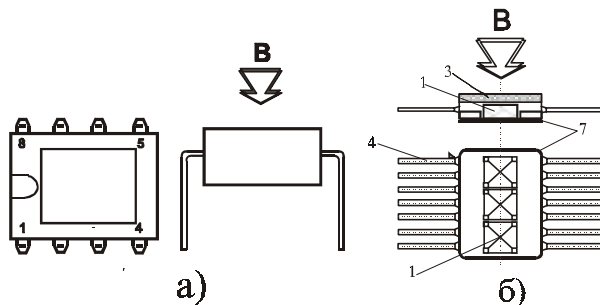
Варианты размещения элементов Холла в стандартных корпусах ИС: а – пластмассовом DIP корпусе; б – в металлостеклянном корпусе
